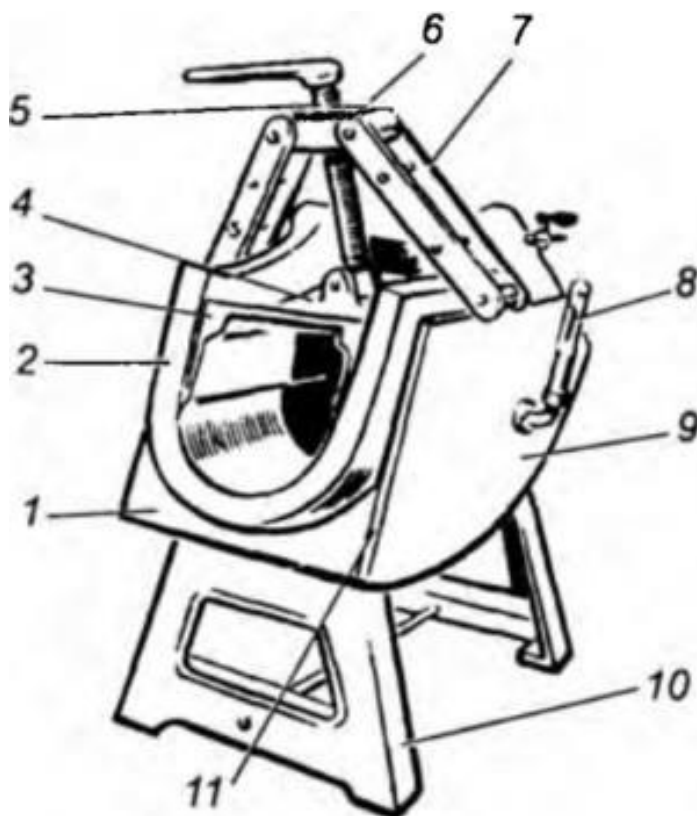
Секторная форма-мульда: 1 — корпус; 2 — паровая рубашка; 3 — бортовые вкладыши; 4 — подпятник; 5 — нажимный винт; 6 — траверса; 7 — струбцина; 8 — термометр; 9 — щиток; 10 — чугунная
